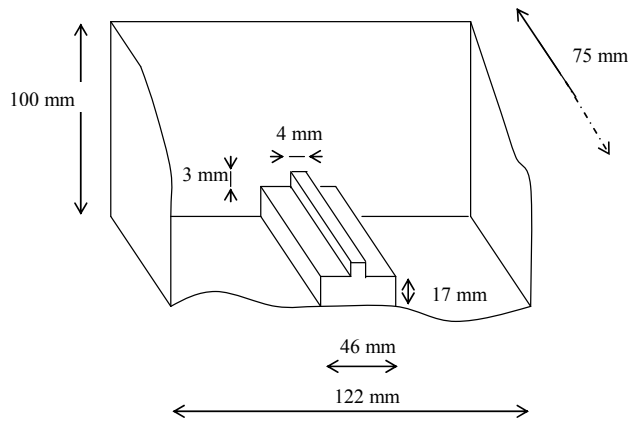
Géométrie du moule (coupe) utilisé pour la réalisation des éprouvettes de clivage. Le dispositif central permet d'obtenir une pré-entaille sur les pièces moulées.
